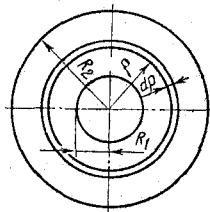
Сечение цилиндрической паковки с элементарным кольцевым слоем
